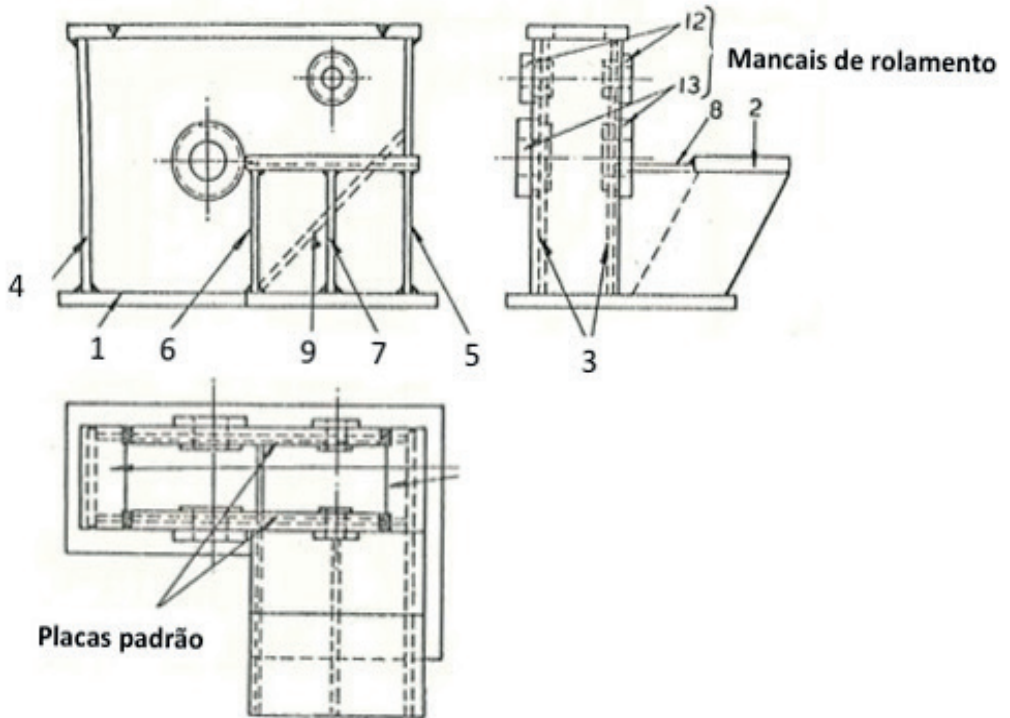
(b) – Layout para placas padrão para caixas de engrenagens soldadas.
